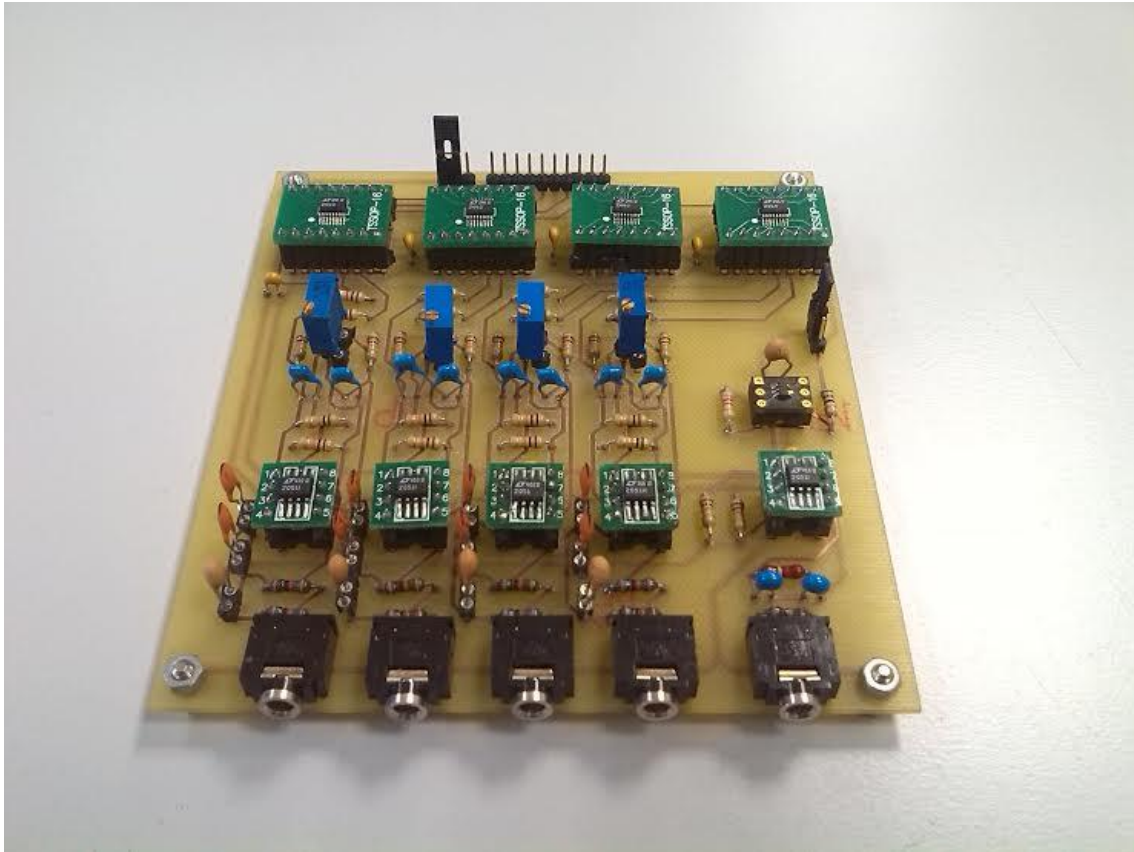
16. Cara de montaje (TOP) de la PCB.
